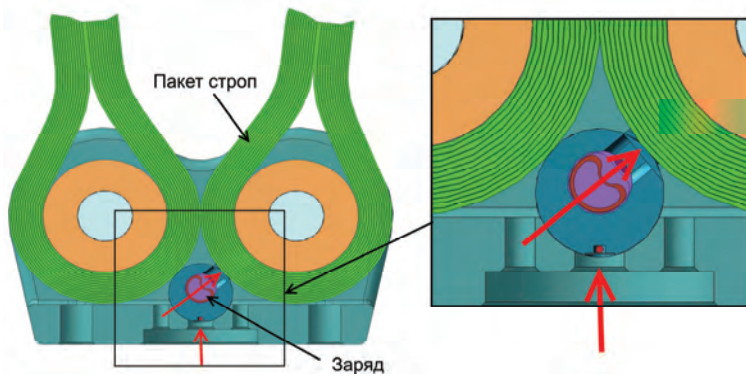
Схема расположения ДУЗ в корпусе вертлюга
